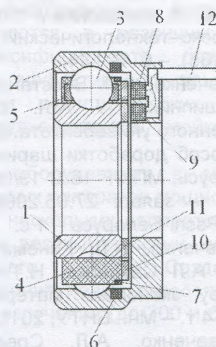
Конструкция подшипника с управляемой кинематикой
